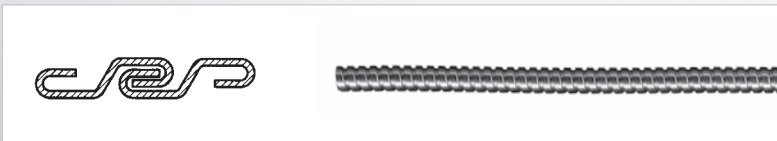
Wickelschlauch mit Agraff-Profil
